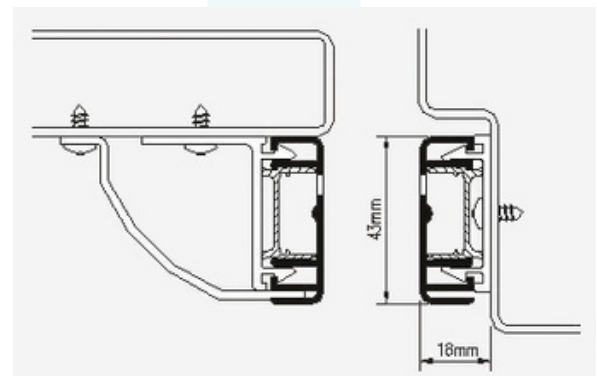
Profilo da 43 mm in apertura laterale con supporto a "L" con protezione e altro supporto in postazione fissa
